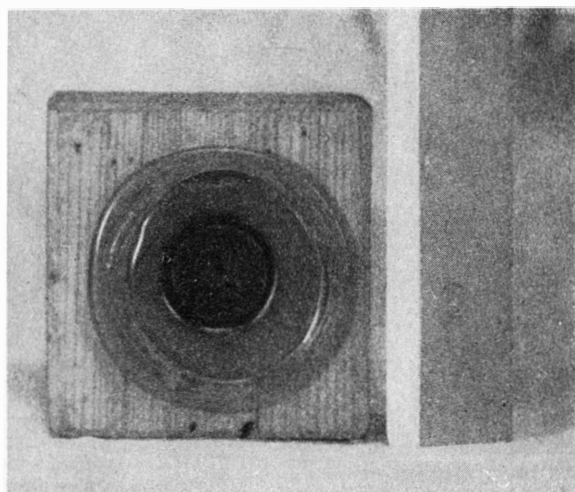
Après écrasement du tube, vue de la collerette qui vient de se former.
